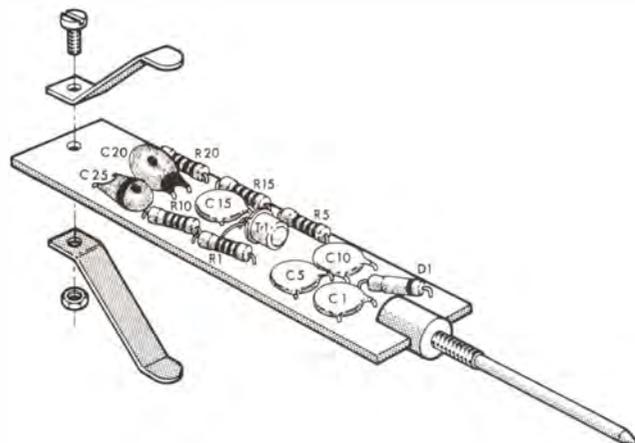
Altro prospetto della sonda con tutti i componenti già posizionati sulla basetta.
